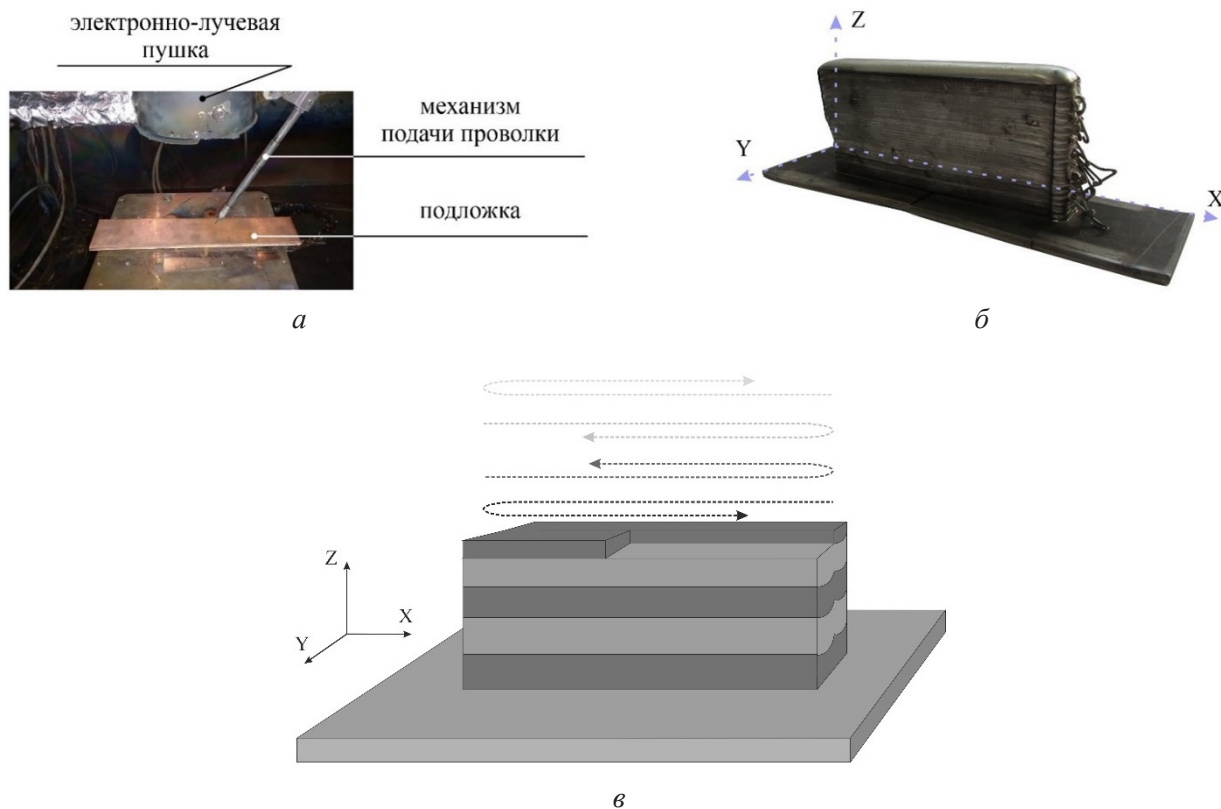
Рабочая область лабораторной установки (*a*), внешний вид (*б*) образца Inconel 625 и схема сканирования (*в*)
